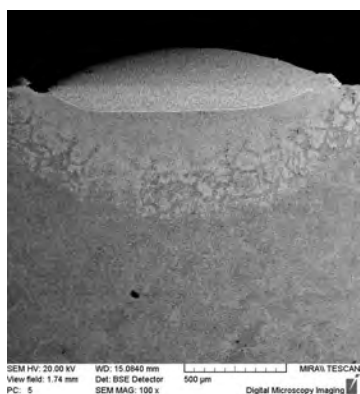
Поперечный шлиф валика, полученного лазерной наплавкой сплава ПГ-12Н-01 при скорости наплавки $V=40$ мм/мин и дистанции наплавки $L=10$ мм
